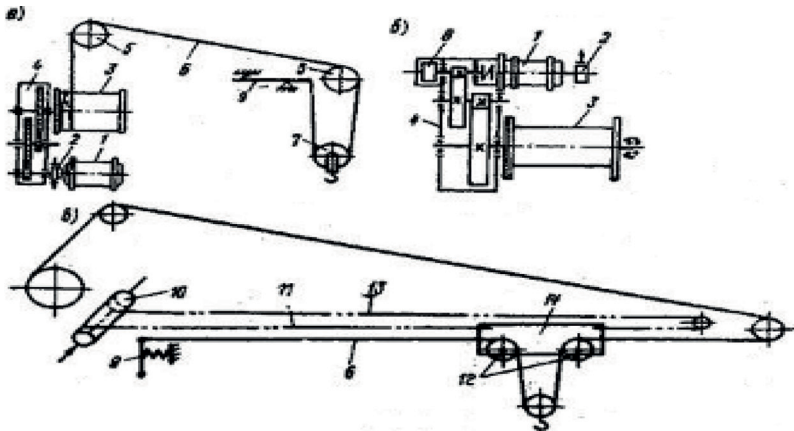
Схемы грузоподъемных механизмов башенного крана
